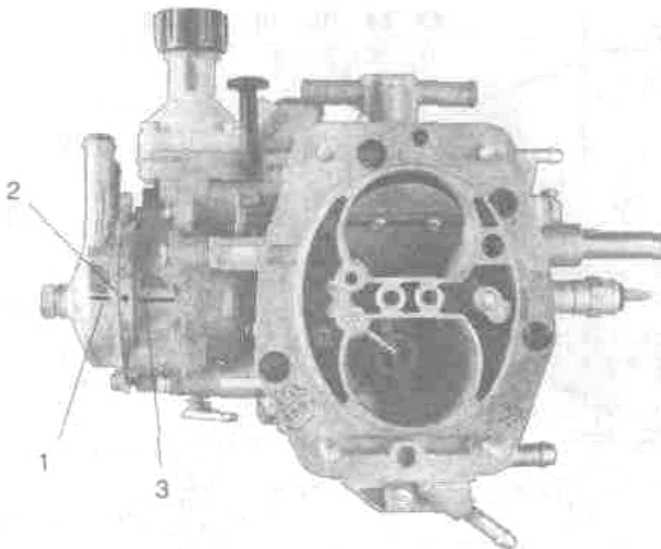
Вид на карбюратор 21083 1107010 62 сверху
